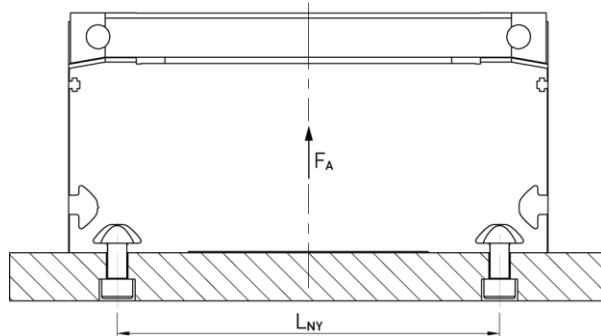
Bohrungsabstand für die Befestigung der Lineartische HT250B von unten mit Nutensteinen
